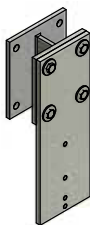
Abstandskonsolle Wandmontage, Variante BT-1
